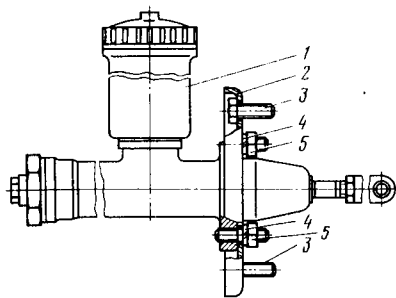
Главный тормозной цилиндр с кронштейном в сборе для установки на унифицированный кузов: 1 — главный тормозной цилиндр; 2 — кронштейн; 3 — болты; 4 — пружинные шайбы; 5 — гайка
